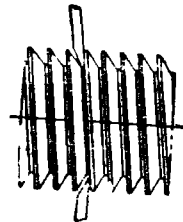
Схема измерения внутреннего диаметра упорной резьбы.
